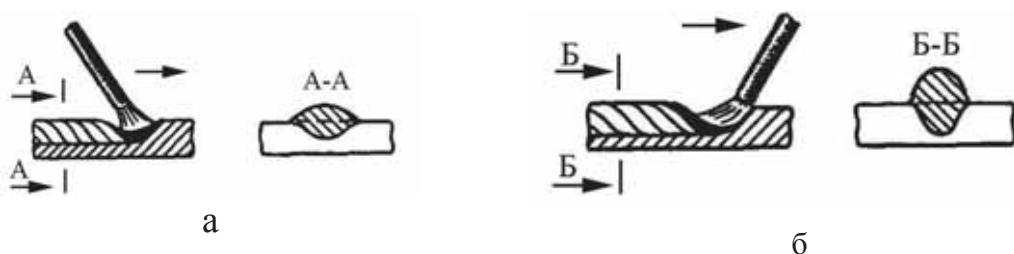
Влияние наклона при сварке на форму шва:
